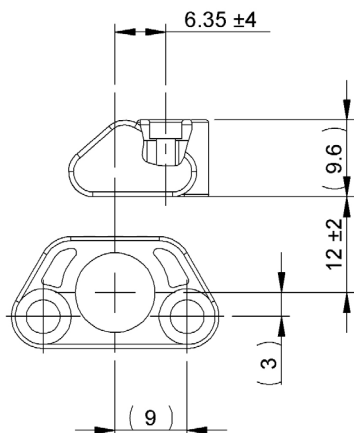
Distancias con sensor de posición BAM TG-MP-028
